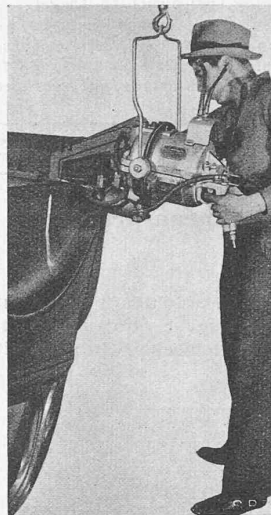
Transportable Punkt-Schweissmaschine
